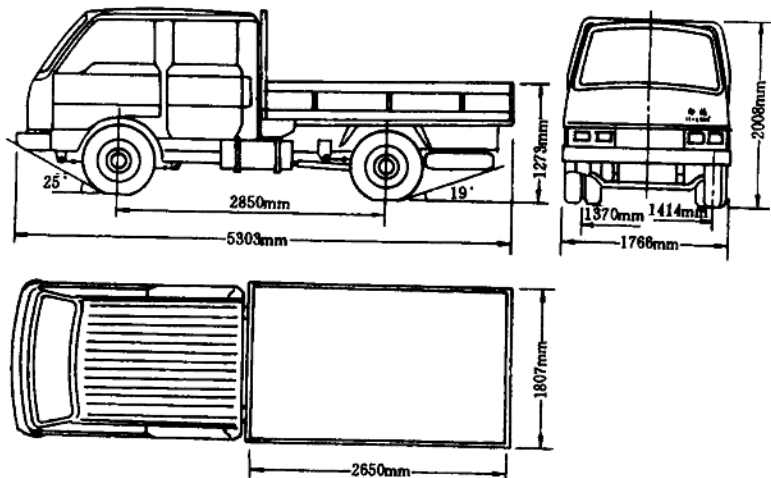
2 解放 CA1046L 型载货汽车外形尺寸
